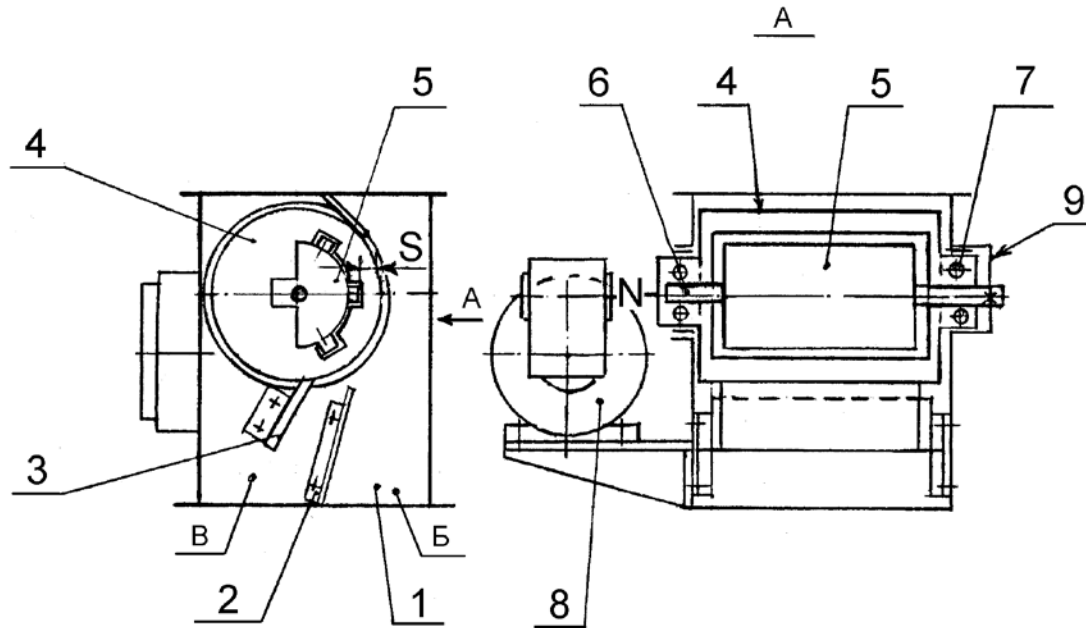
Магнитный сепаратор: 1 – корпус; 2 – перегородка; 3 – скребок; 4 – барабан; 5 - магнитная система; 6, 7 - опоры; 8 – привод
